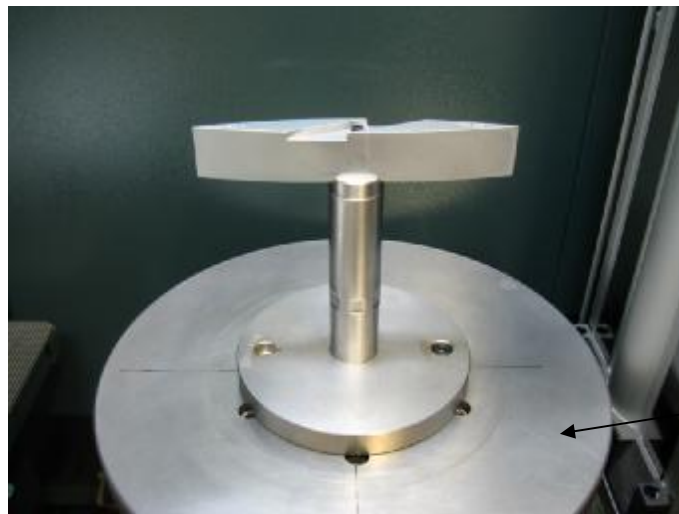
Общий вид меры-имитатора пера лопатки
